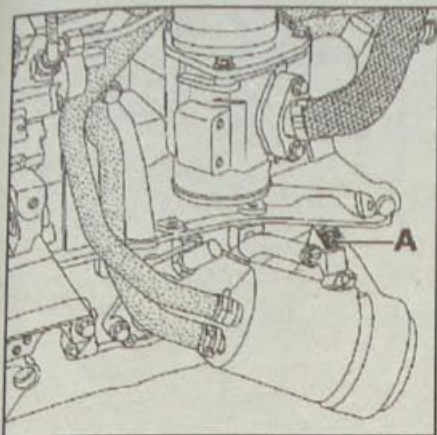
Расположение пробки (А), закрывающей отверстие для установки фиксатора коленчатого вала
